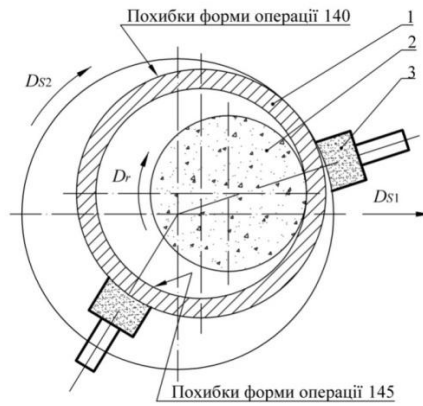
Схема шліфування доріжки кочення кільця зовнішнього: 1 – заготовка кільця; 2 – головка шліфувальна; 3 – опори
